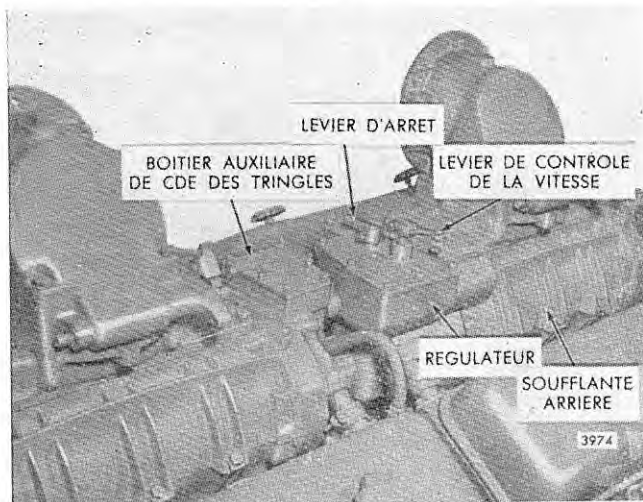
V-1 - Montage du régulateur et du boîtier auxiliaire
